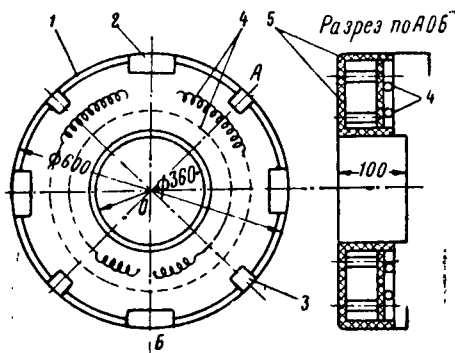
Кольцевая электропечь для нагрева вентиляторов тяговых двигателей ДК-103А и ДПИ-150:
